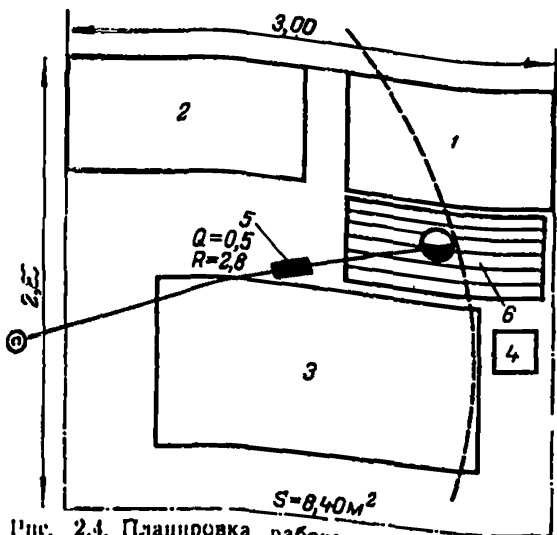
Планировка рабочего места слесаря-ремонтника по разборке узлов станка:
